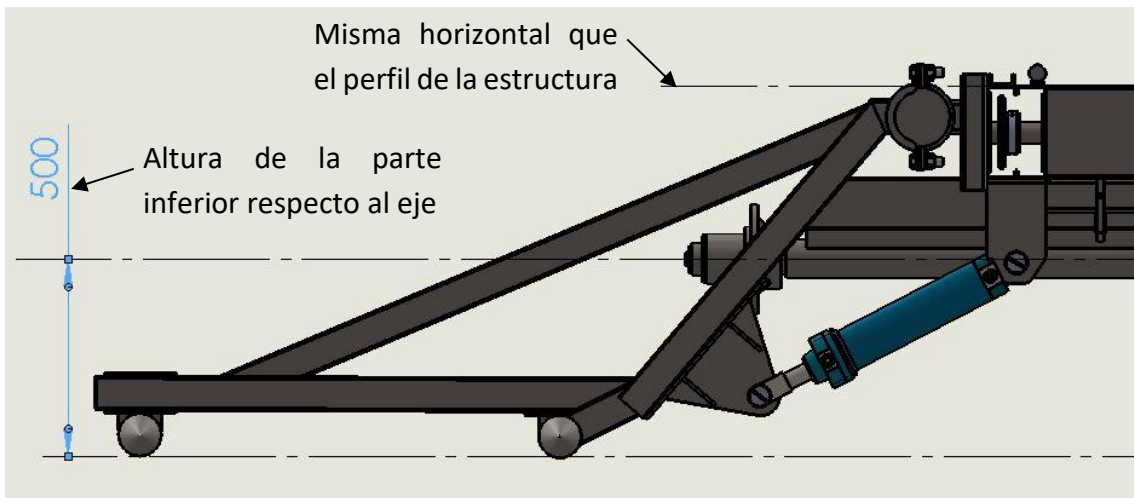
Posicionamiento y dimensiones del conjunto pinche
